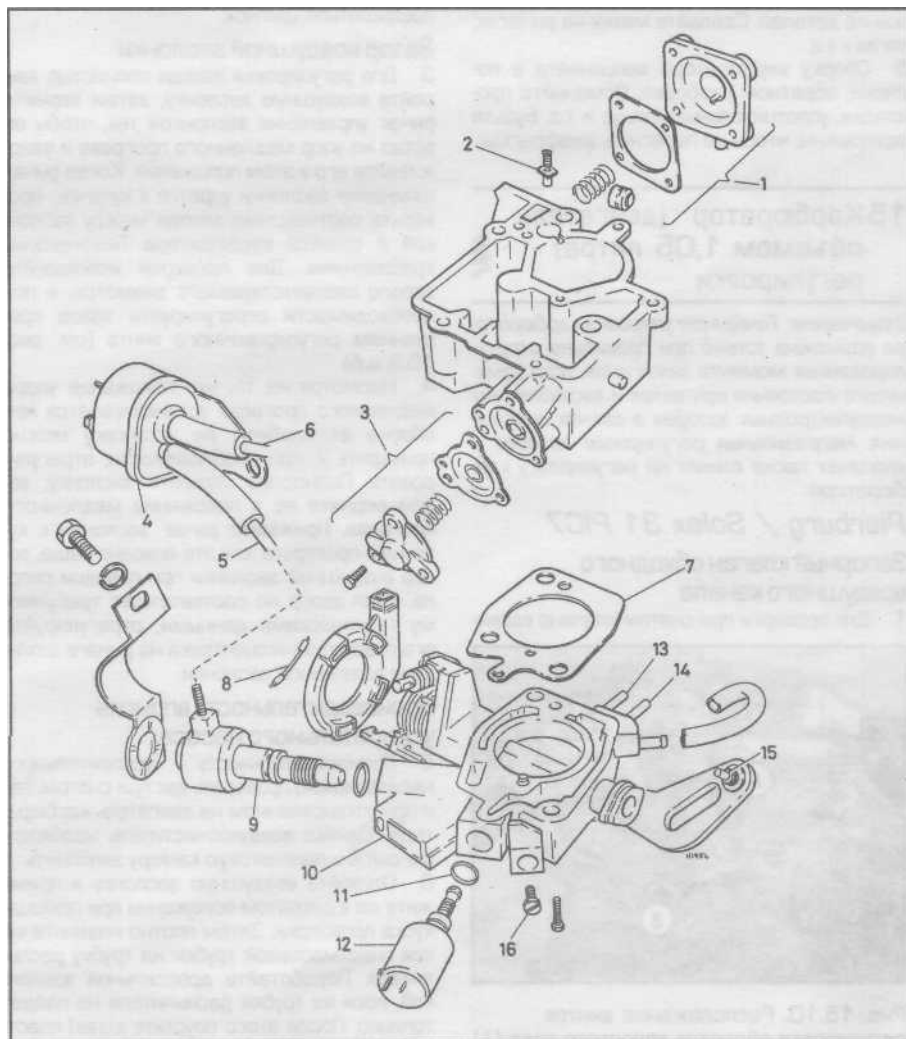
, ж. Детали корпуса карбюратора Weber 32 TLA
